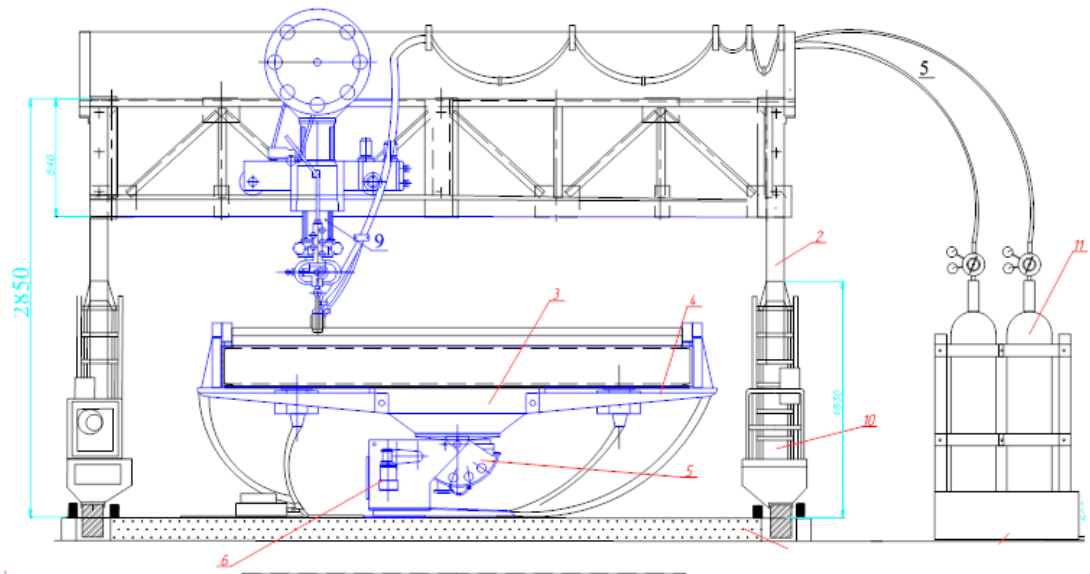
Установка для зварювання листів обшивки з каркасом
